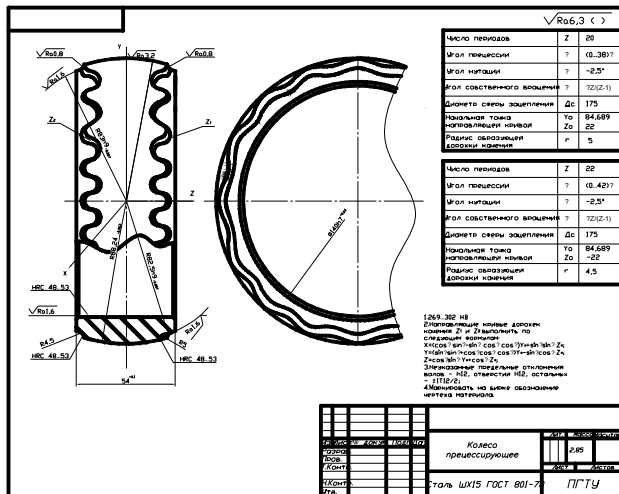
Чертеж детали "Колесо прецессирующее"
